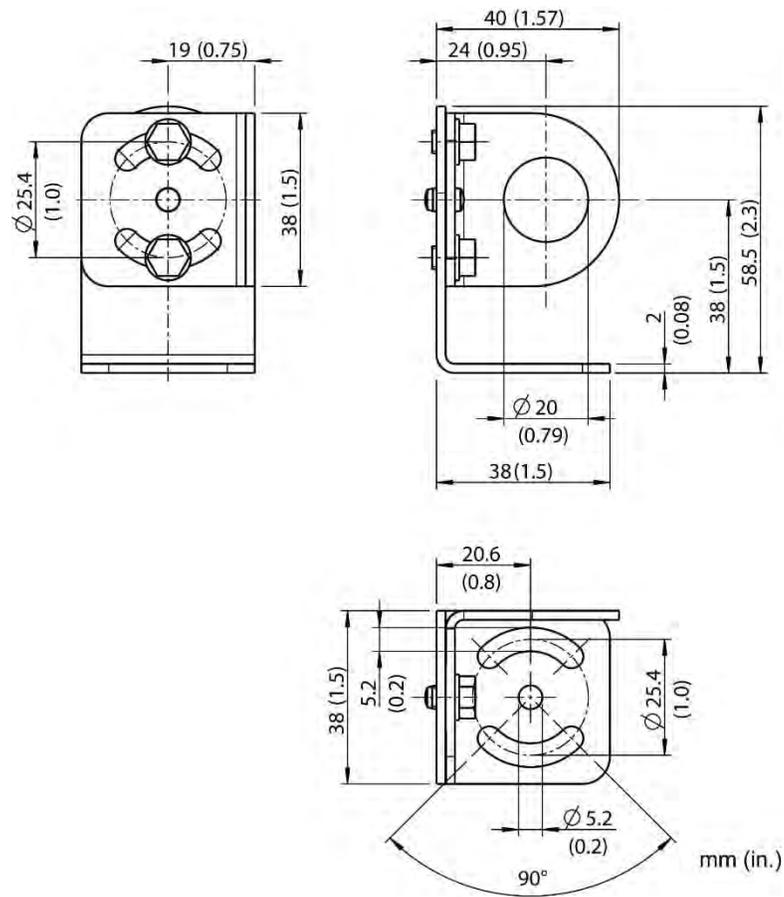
Dimensions de l'équerre de montage ajustable (XXXMI3100ADJB)
